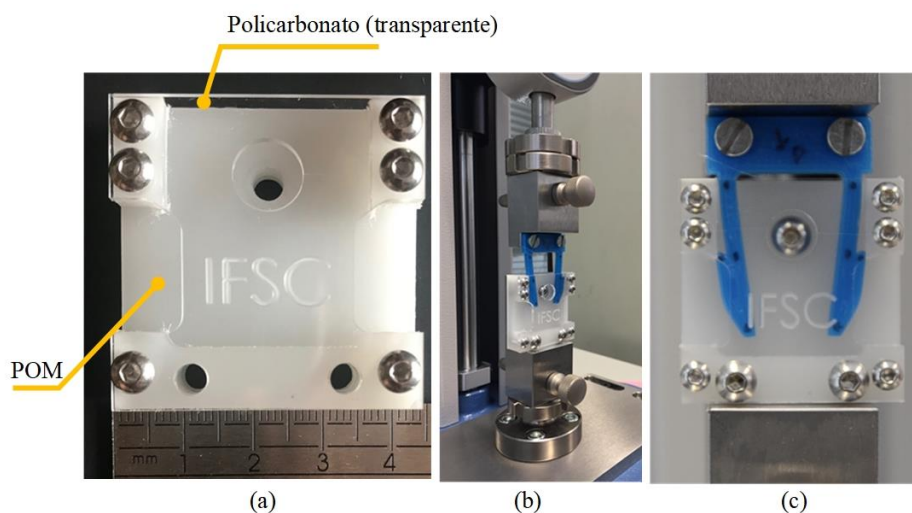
Módulo de teste (a), montagem na máquina de ensaios (b) e teste de montagem (c).
